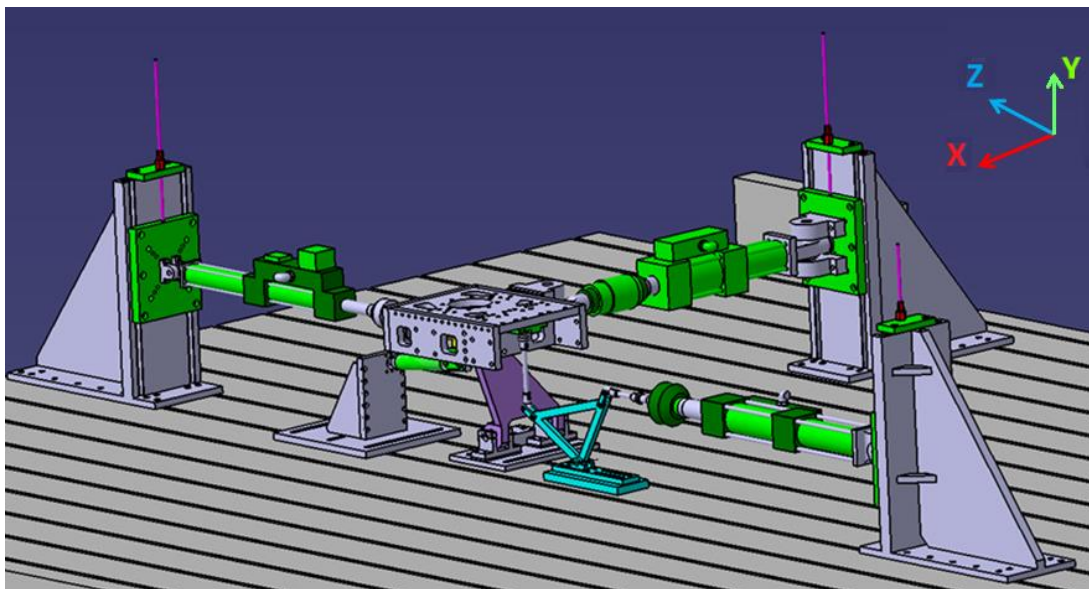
Layout de la disposición Longitudinal en Catia. Vista 2
